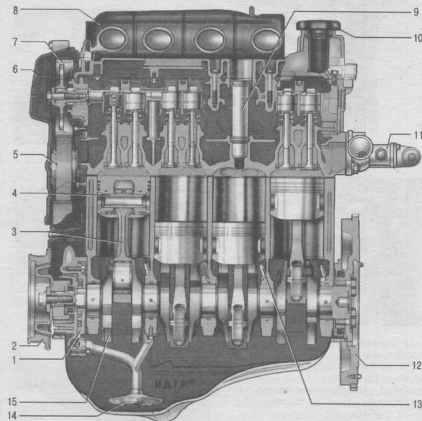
Продольный разрез двигателя ВАЗ-11194: 1 — масляный насос; 2 — шкив привода генератора; 3 — шатуны; 4 — поршневой палец; 5 — ремень привода газораспределительного механизма; 6 — крышка газораспределительного механизма; 7 — шкив распределительного вала; 8 — впускной коллектор; 9 — свечной колодец; 10 — крышка маслоналивной горловины; 11 — термостат; 12 — маховик; 13 — форсунка охлаждения днища поршня; 14 — маслоприемник; 15 — коленчатый вал
